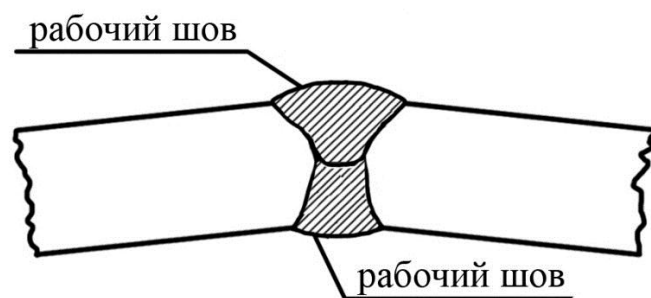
Сварка рабочих швов с наружной и внутренней стороны трубы
